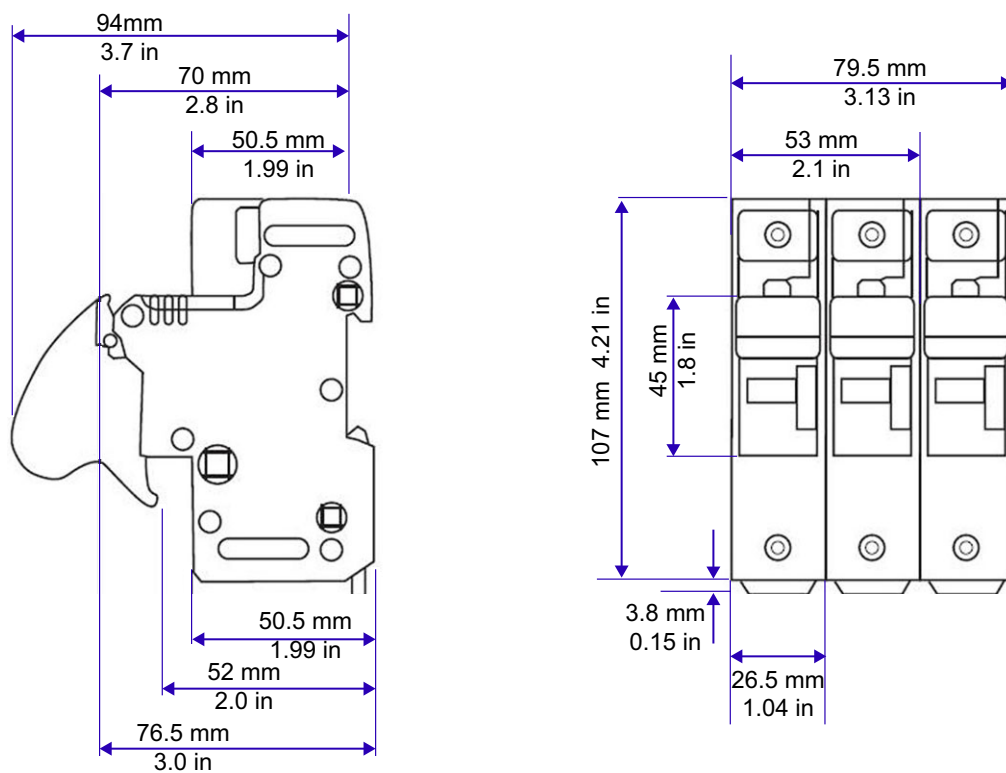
Dimensioni dei portafusibili: US143 (14x51 mm)
